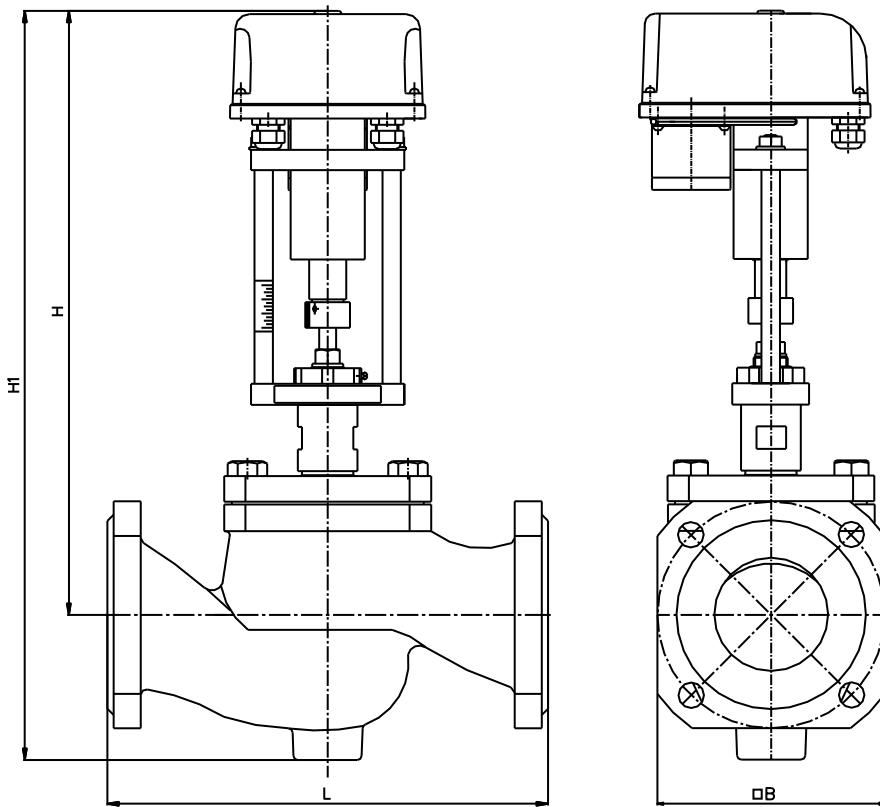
Габаритные установочные и присоединительные размеры клапана.
